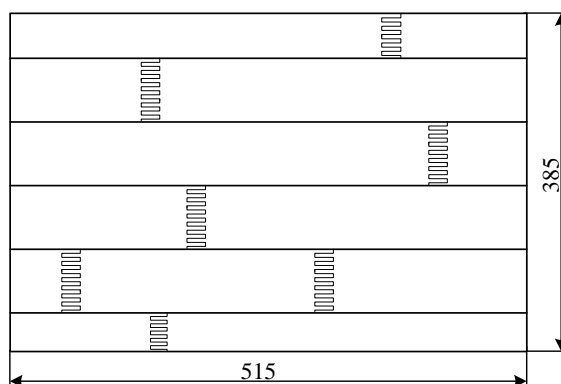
Заготовка для дверной филенки (мебельный щит)
